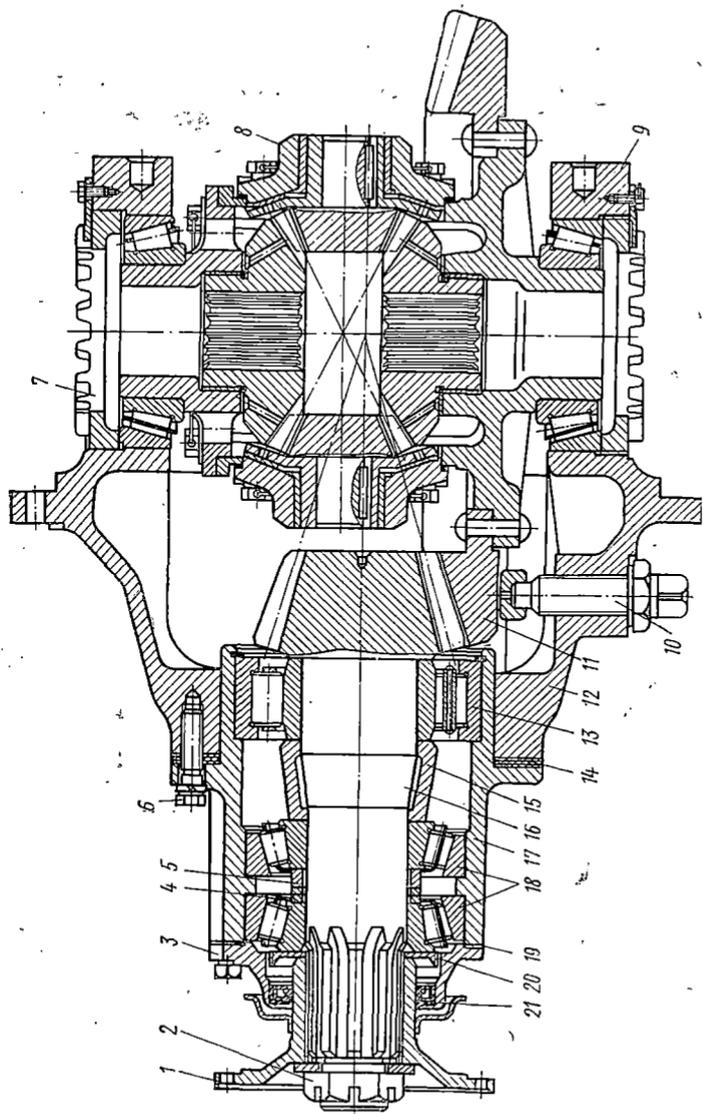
Редуктор ведущего моста самоходного скрепера ДЗ-11М:
